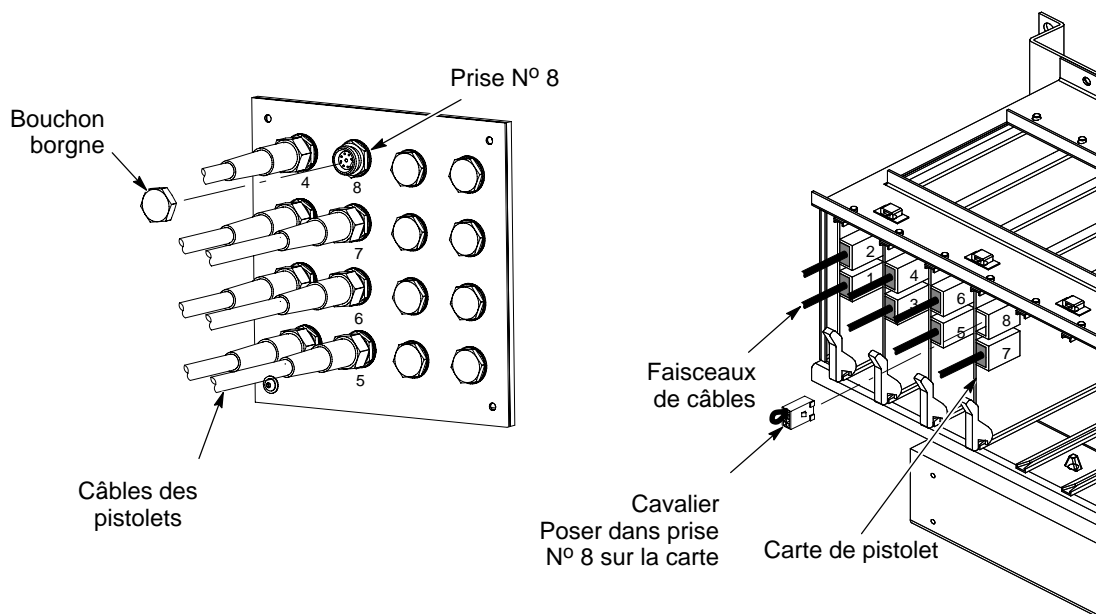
Pose du bouchon et du cavalier – Exemple illustrant un système à 8 pistolets avec 7 pistolets
